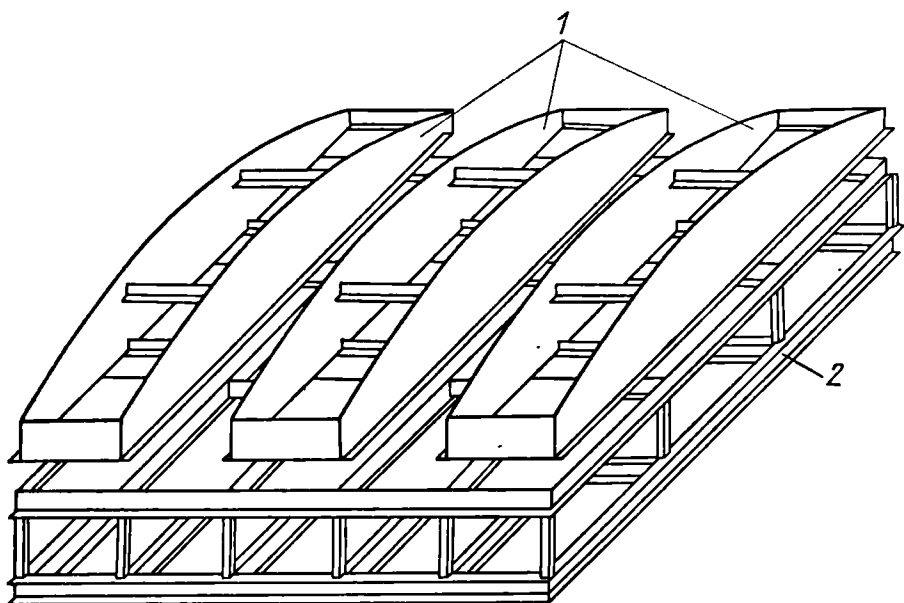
Постель для сборки и сварки бортовых секций.
